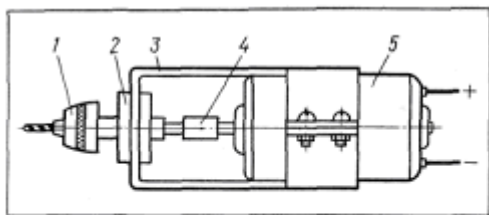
Приспособление для сверления отверстий малого диаметра:
